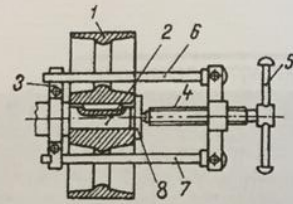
Dispozitiv de montare a roții de curea: 1 - roată de curea; 2 - arbore; 3 - bridă fixată pe arbore; 4 - șurub de presare; 5 - manivelă; 6, 7 - pârgșii; 8 - placă de presare.
